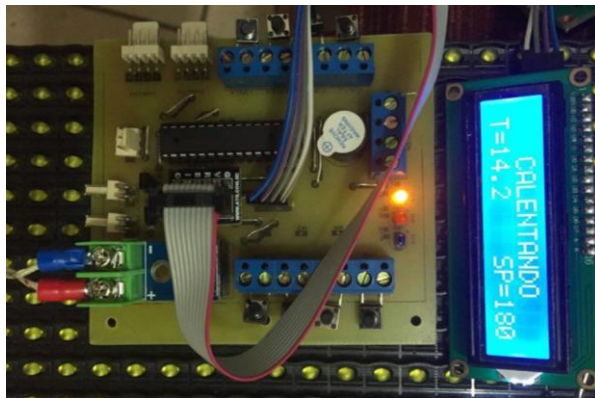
Instalación y soldado de componentes electrónicos en la placa.
